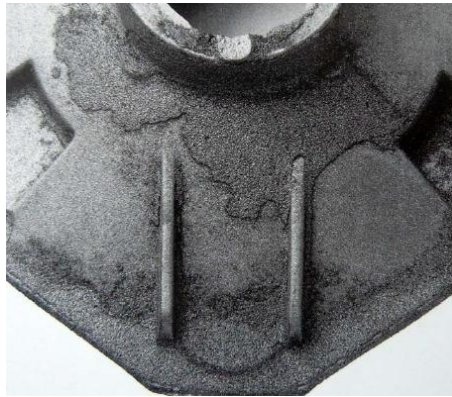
Mechanismus penetrace způsobené explozí vody [38].
